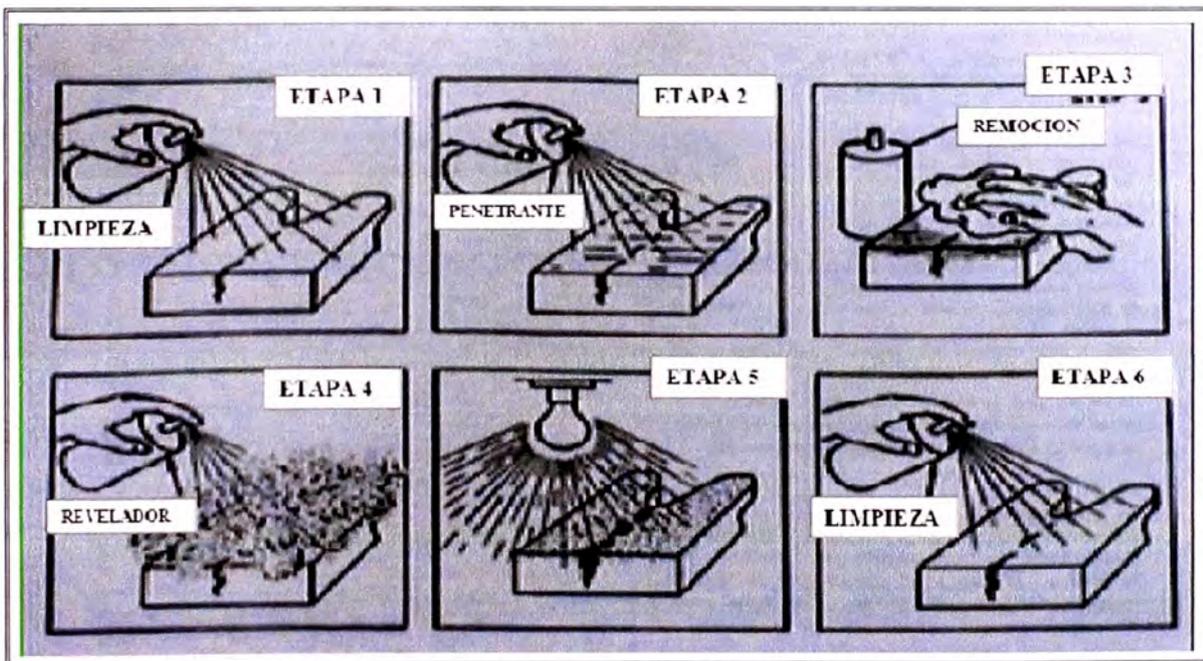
Etapas del Ensayo por Líquidos Penetrantes
